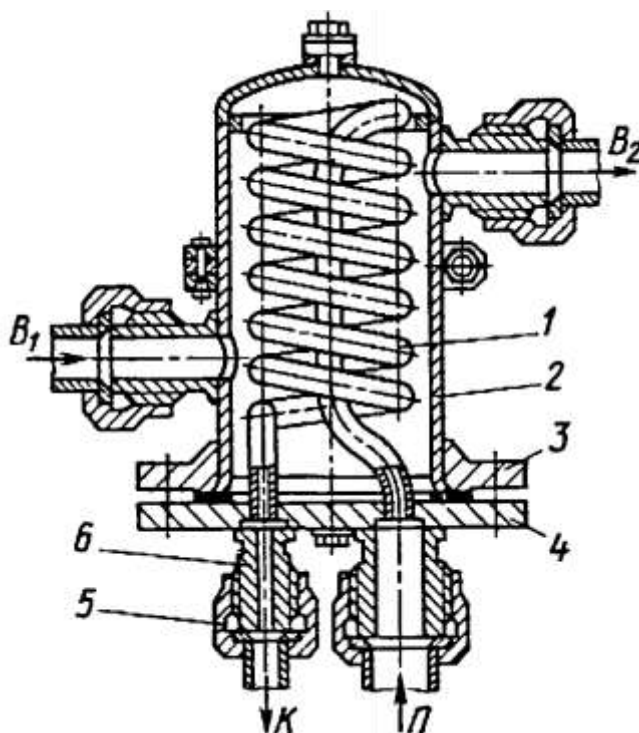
Нагреватель змеевик: 1 – Змеевик; 2 3 – корпус фланца 4 – крышка; 5- гайка 6-корпус; 6 – сопло. B1 – подвод воды; B2 – выход воды; P1 – ввод номинала; P2 – выход конденсата.
